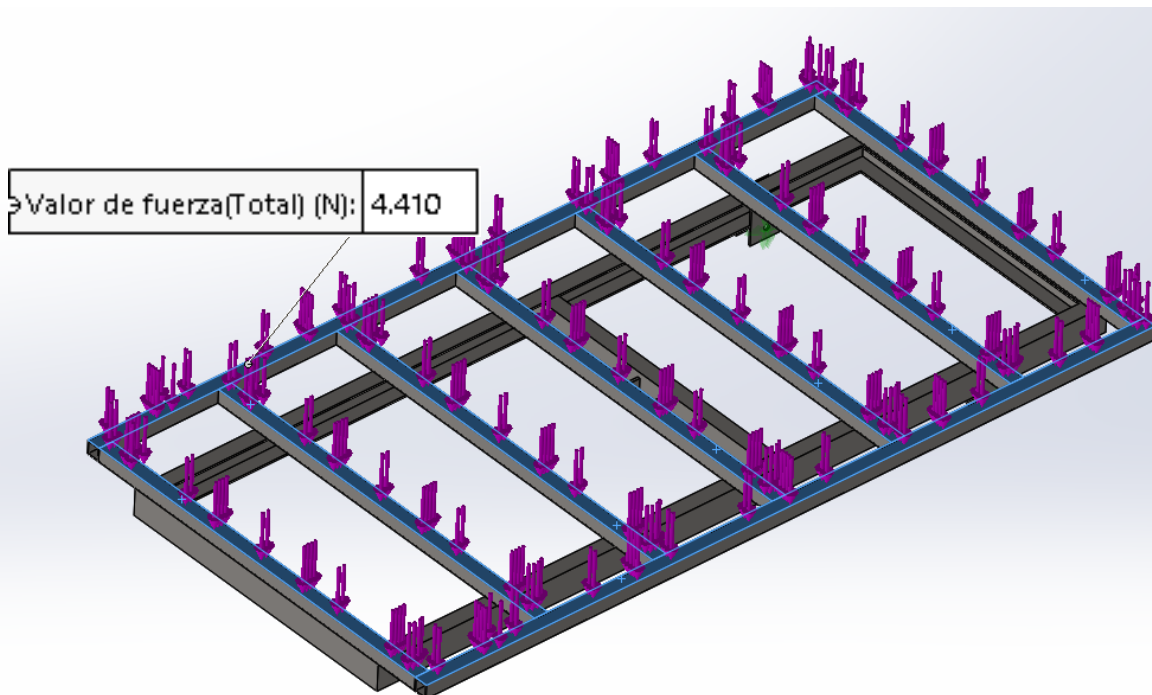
Carga que puede llevar el remolque aplicada sobre la superficie del chasis.
